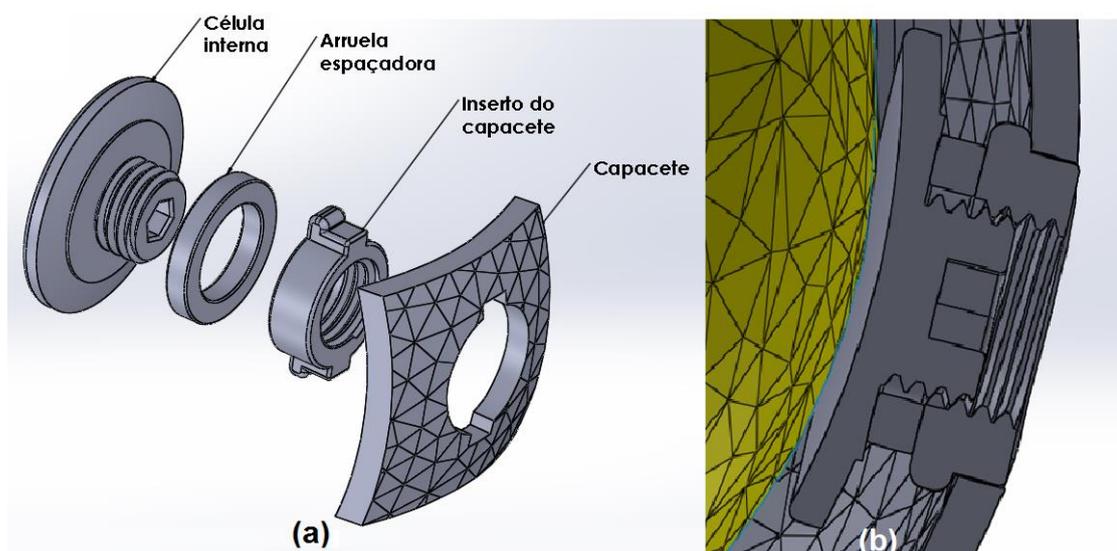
Quinto mecanismo de ajuste desenvolvido em vista (a) explodida e (b) em corte inserido no capacete.
